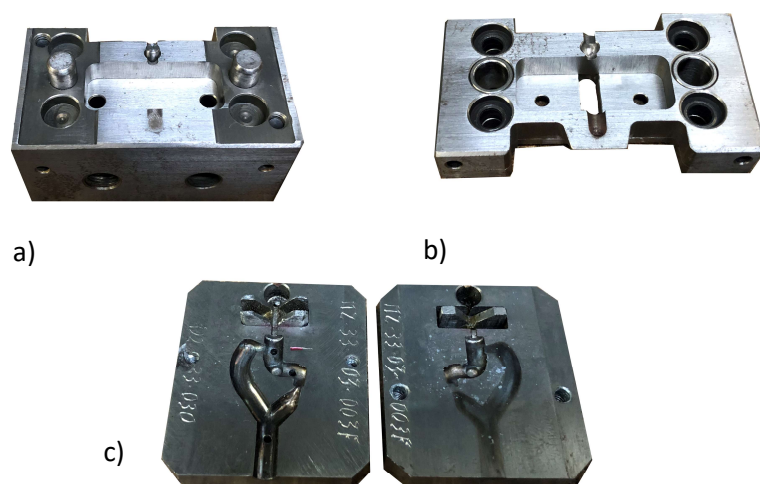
a) Estrutura superior; b) Estrutura inferior; c) Moldes
